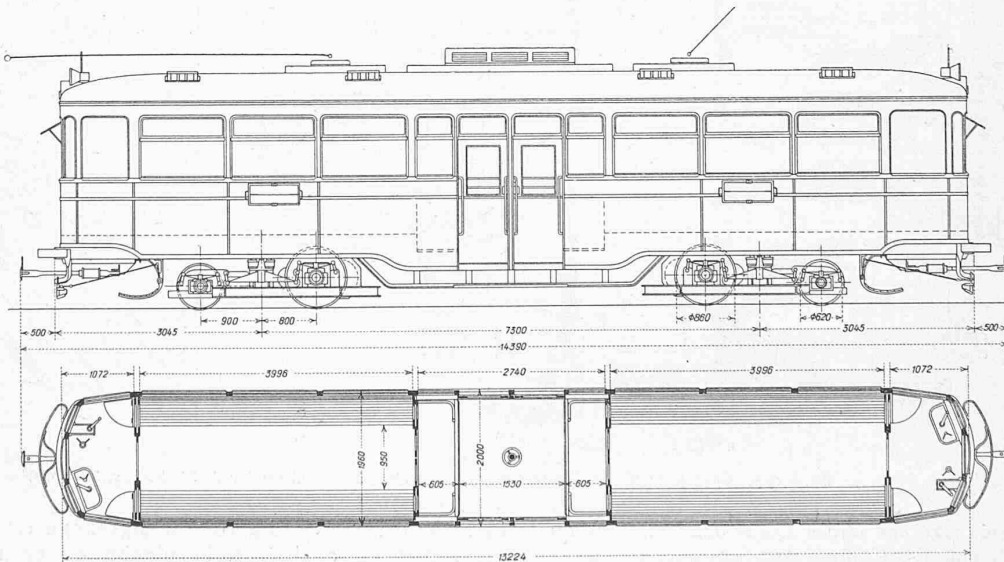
Elevation et plan de la voiture motrice à quatre essieux, avec entrée centrale. — Echelle de 1 : 100.
